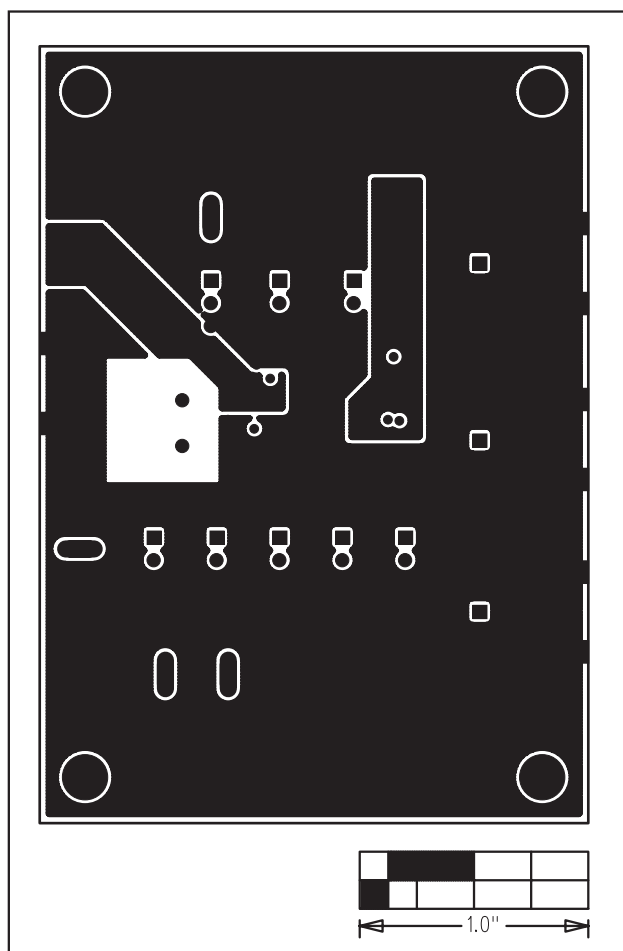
MAX9485 评估板PCB 布局—焊接层
